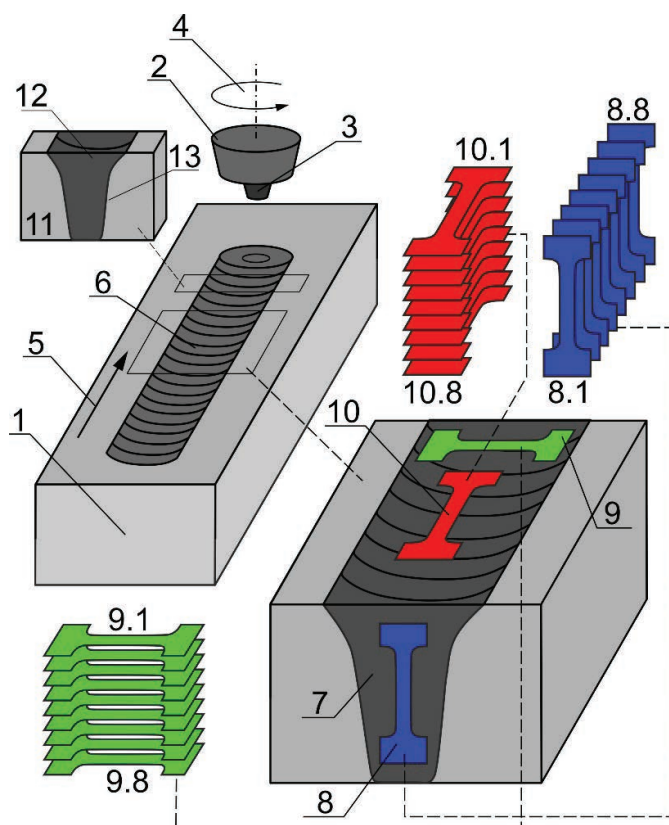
Схема процесса сварки трением с перемешиванием и вырезки образцов для механических испытаний и поперечных шлифов:
